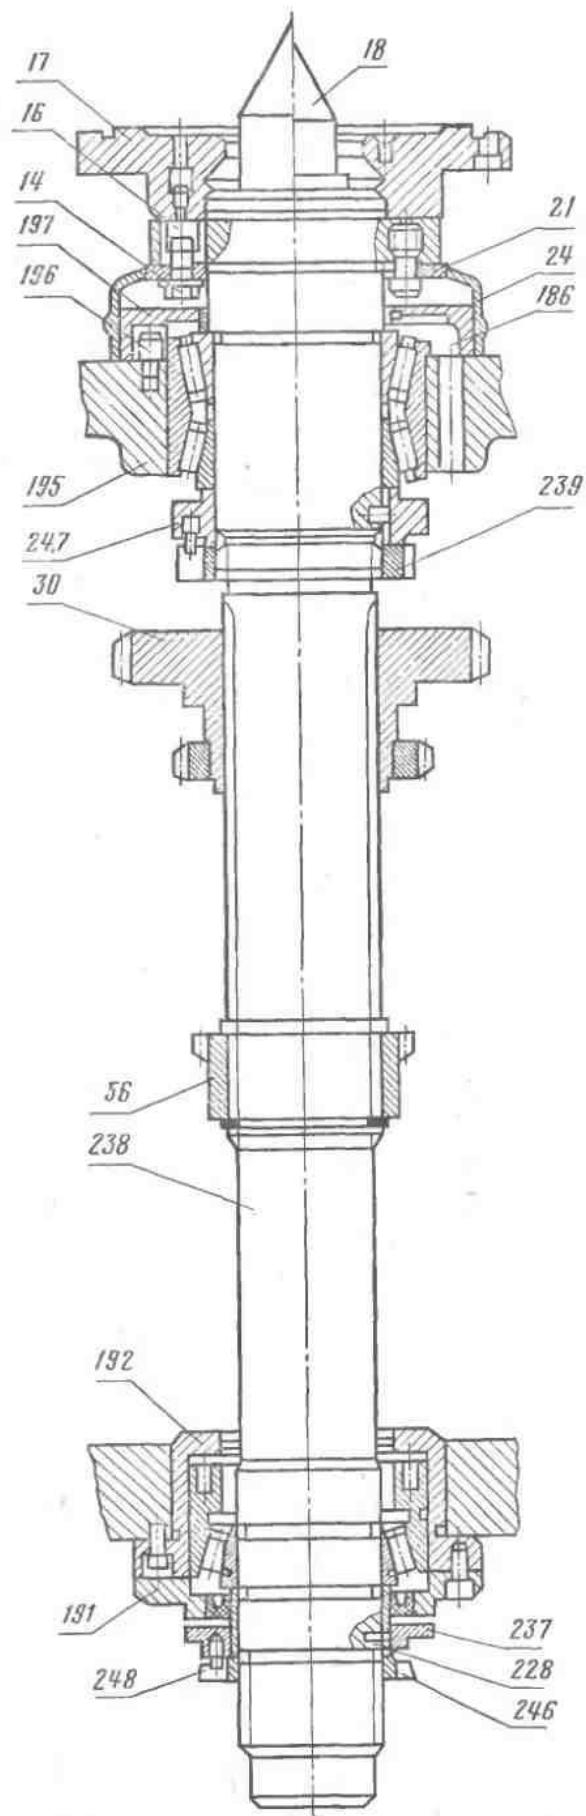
Шпиндельная бабка (чертеж шпинделя в сборе)
